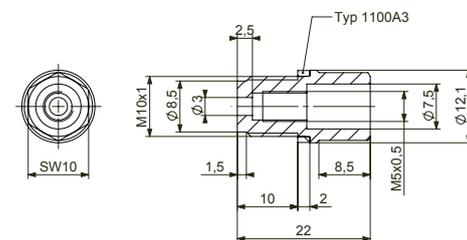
Motorenadapter M10 Typ 6595A1Q01
